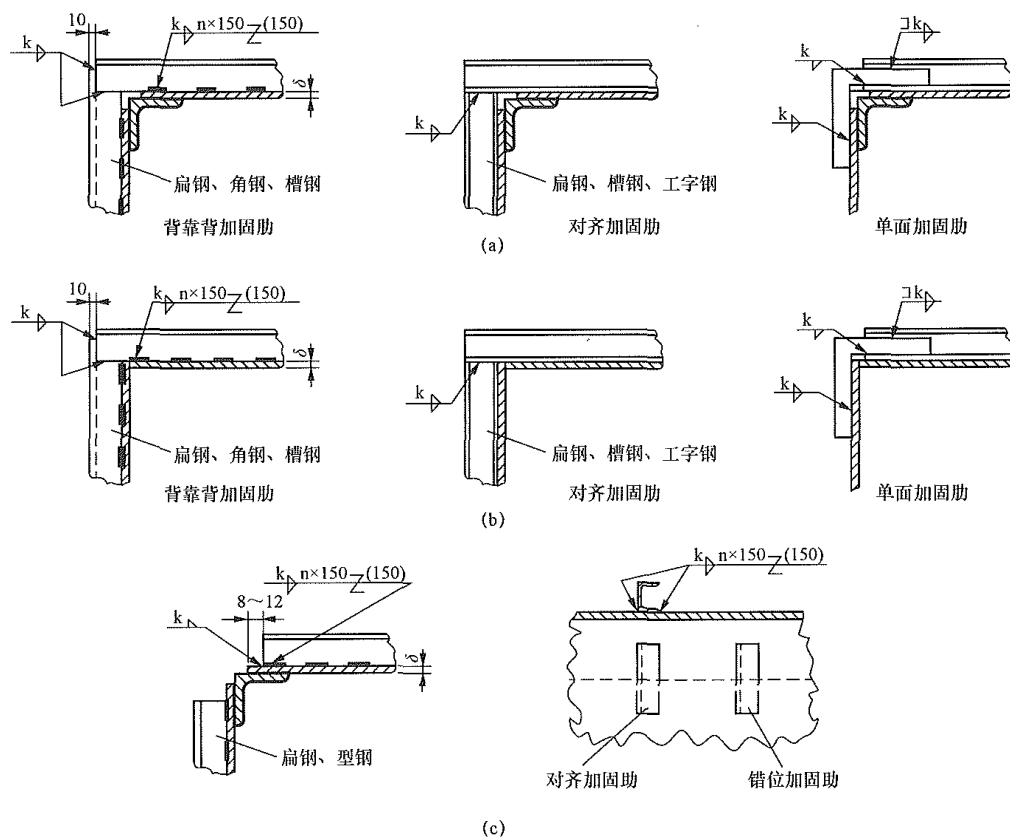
矩形道体的加固肋焊接 (mm)
